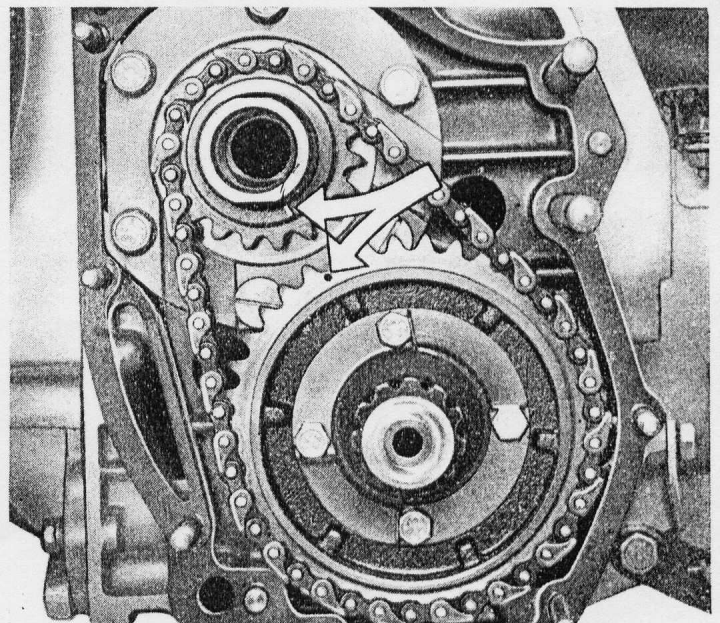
Bezugszeichen an den Steuerrädern für die Einstellung der Steuerung.
